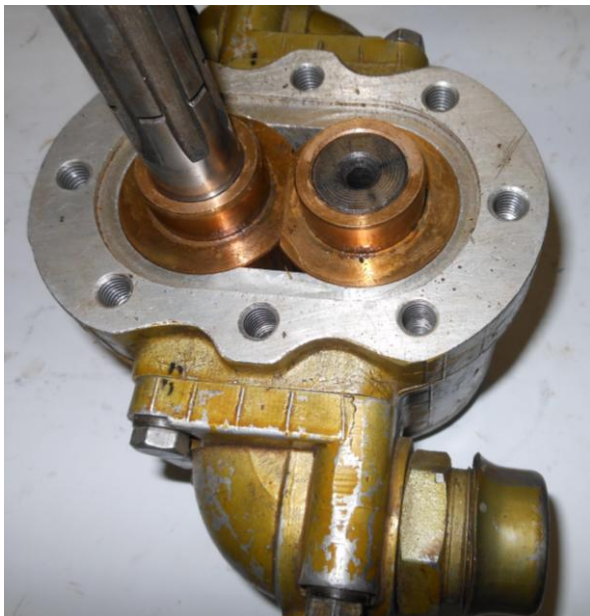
Установка втулок подшипников на шейки валов-шестерен
